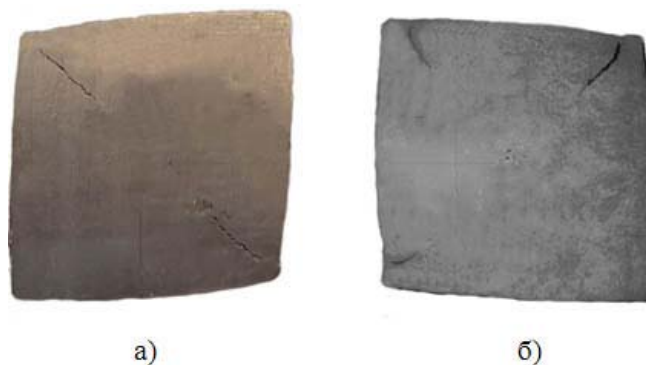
Внешний вид темплетов непрерывнолитых заготовок при развитии явления ромбичности
